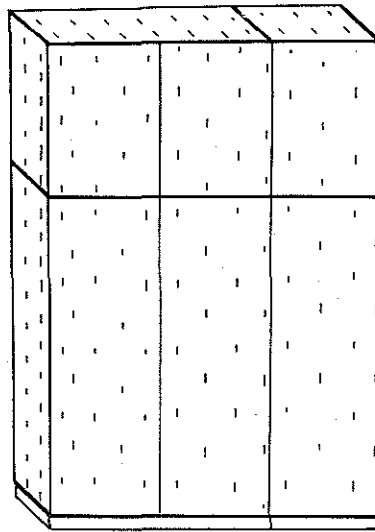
Изометрический вид каркаса изделия корпусной мебели, разработанный с помощью ЭВМ.
